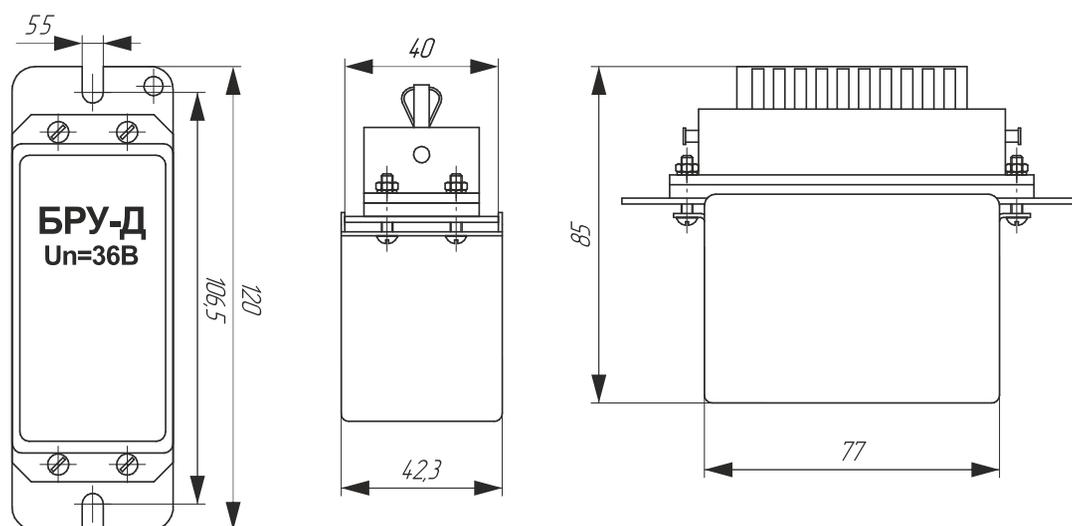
Габаритные и присоединительные размеры блока БРУ-Д
